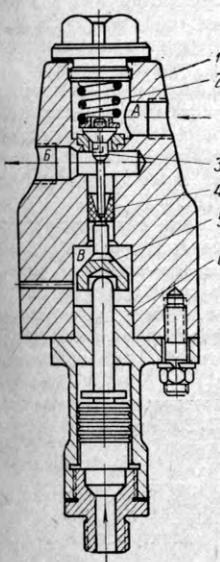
Запорный клапан гидропривода вентилятора охлаждающего устройства:
